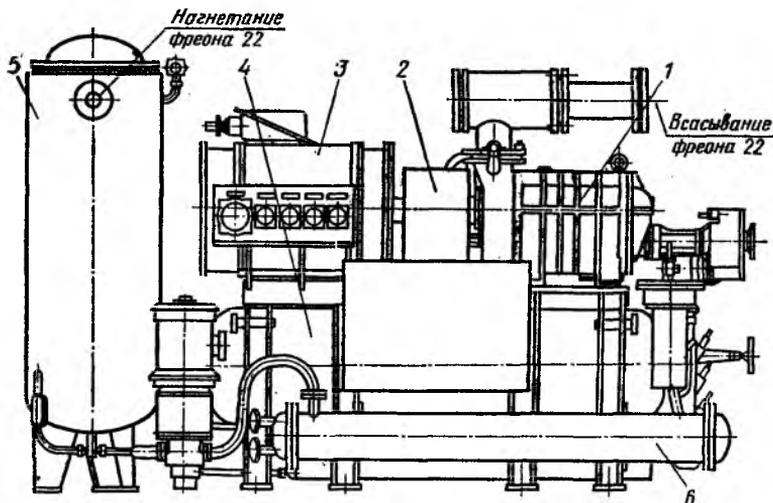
Винтовой компрессорный агрегат 5BX-350/5FC:
